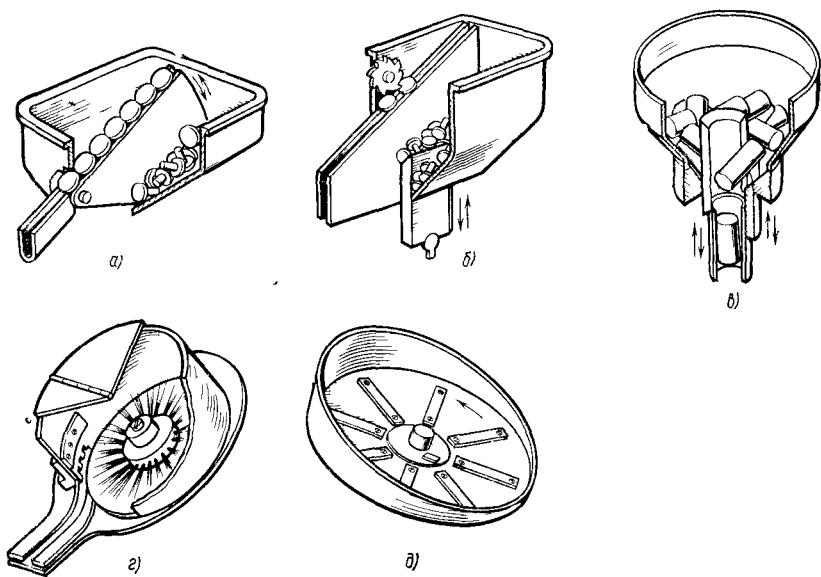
Бункеры для захвата и ориентации группы заготовок
